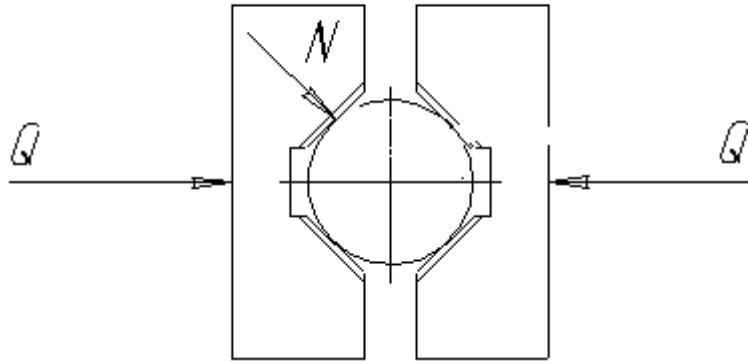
Схема закрепления заготовки на операции 025
